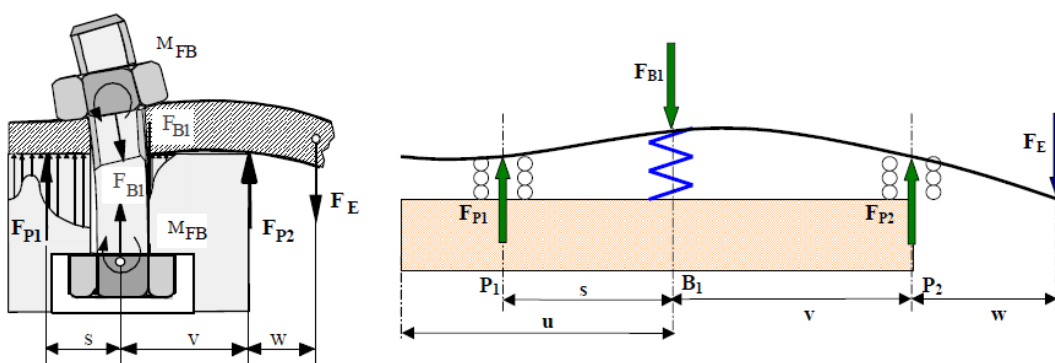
Modèle poutre fléchie [CHA07]
